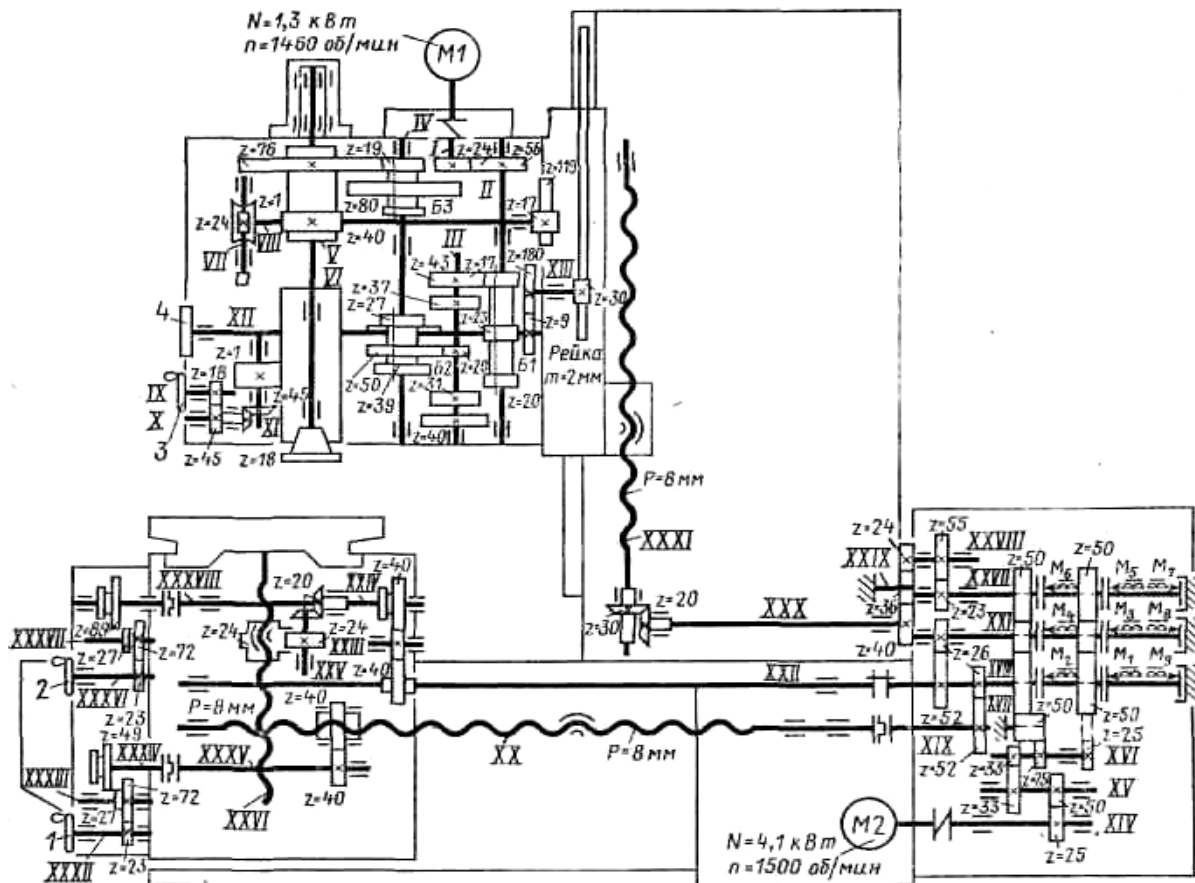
Кинематическая схема вертикально-фрезерного станка модели 6560
